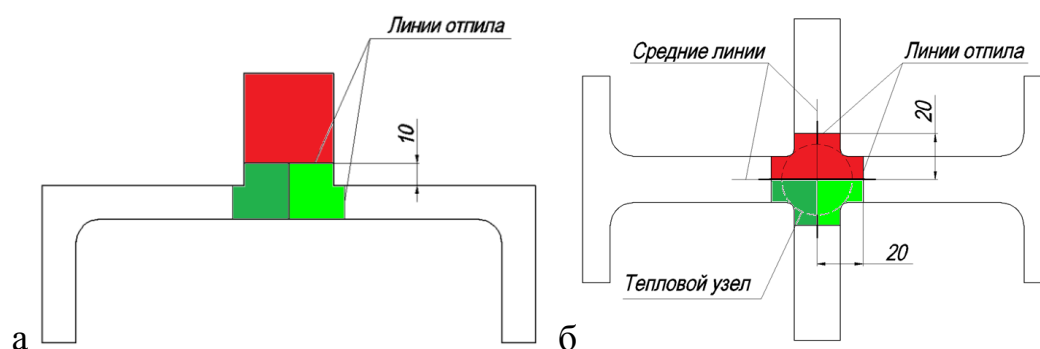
Схема вырезки образцов: а – для проб типа скоба/брус; б – для проб типа «иерусалимский крест». Обозначения: красный цвет – для исследования на томографе; зеленый – для металлографии.
